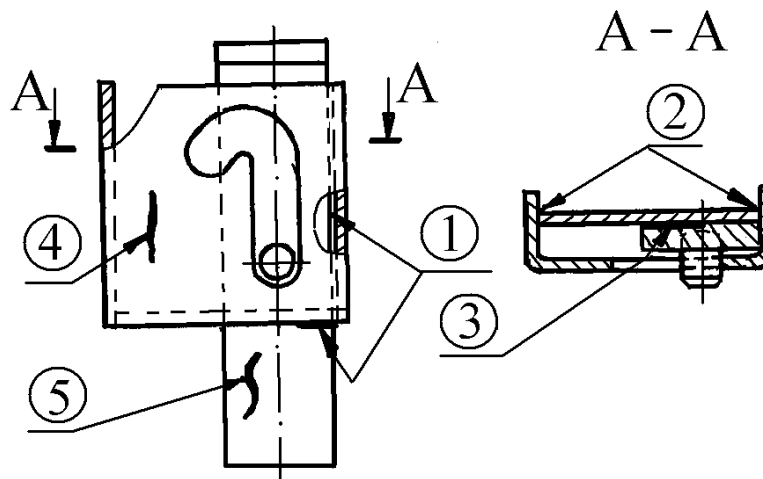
Нижний запорный механизм торцевой двери полувагона
